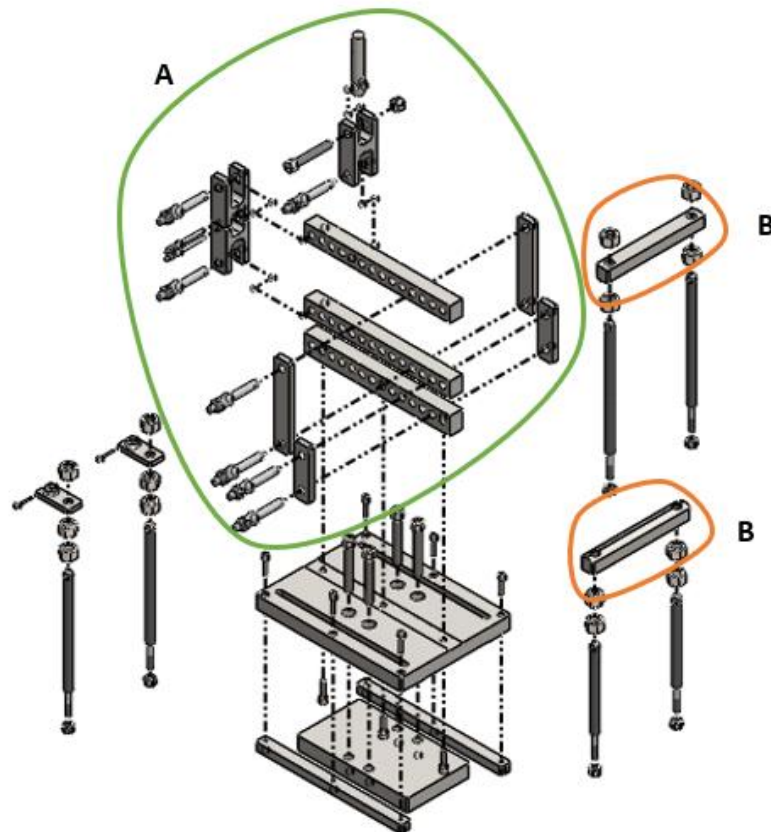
Vista explodida do equipamento MMB desenvolvido
